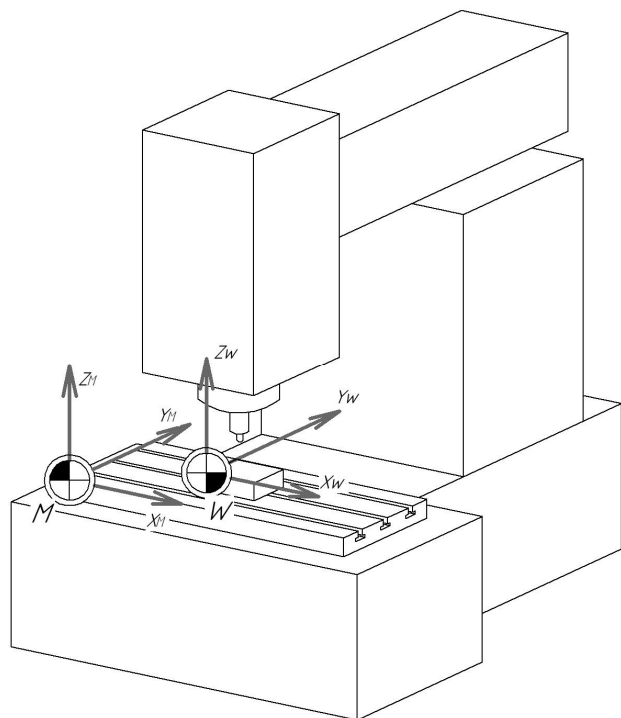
Приклад розташування нульової точки верстата (M) і деталі (W)
